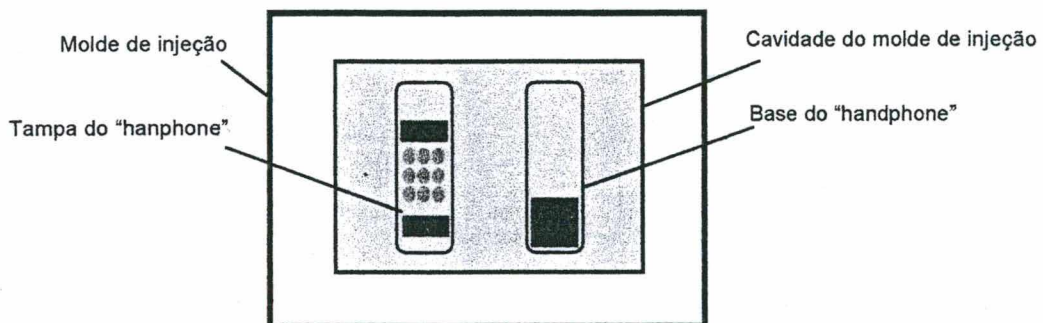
Disposição da base e da tampa do handphone no molde de injeção.
